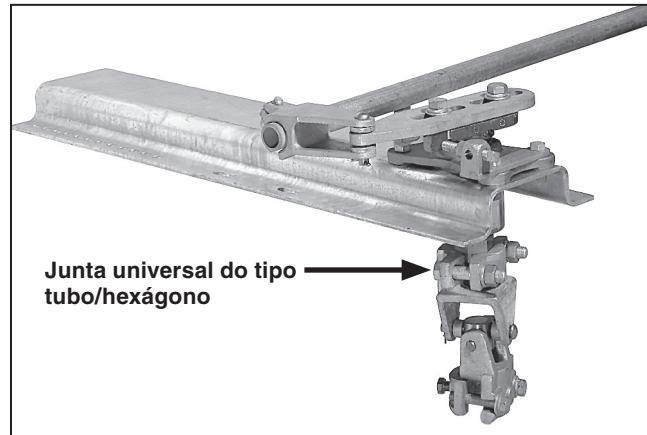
Configuração de ferragens de interligação típica, ferragem de montagem horizontal das unidades-polo da chave.
